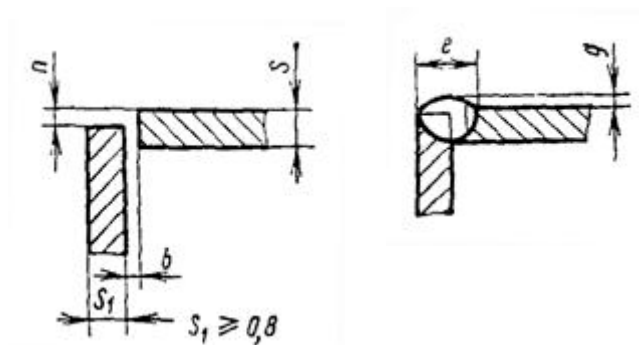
Эскиз сварного соединения У4 ГОСТ 14771-76
